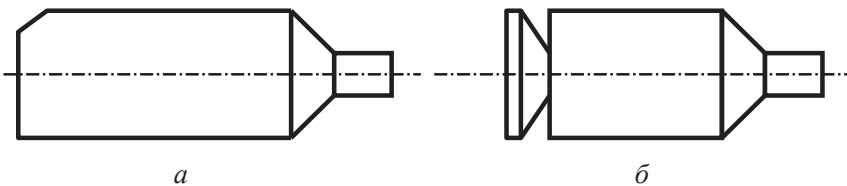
Приемы торможения заготовок нанесением лысок (*а*) и применением пробок-заглушек (*б*)
